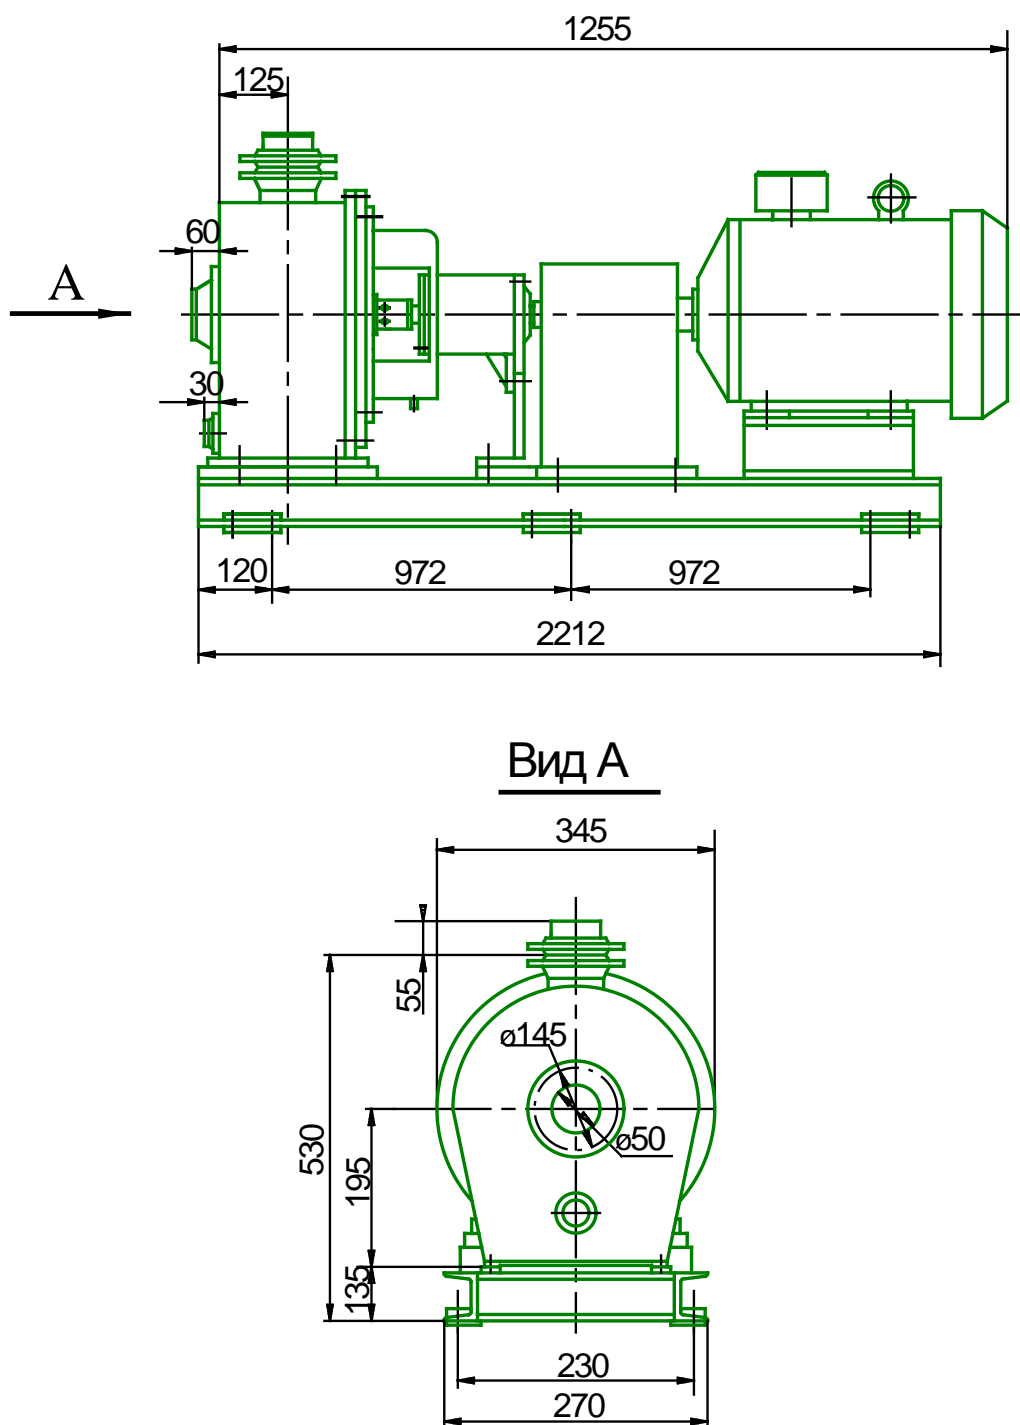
Габаритный чертеж насосного агрегата типа ЦНА 12,5/50
